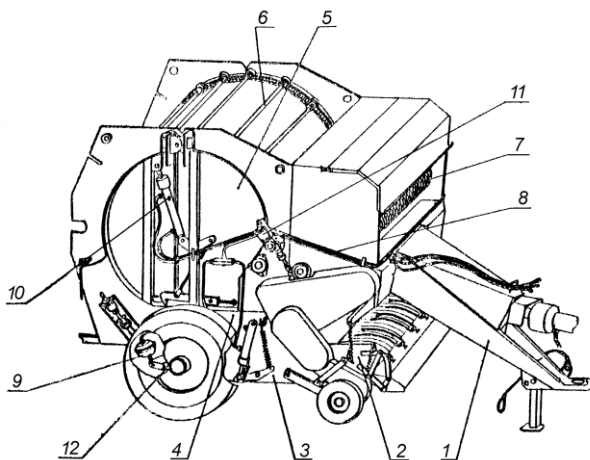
Общий вид пресс-подборщика: 1 – сница; 2 – подборщик; 3 – измельчитель; 4 – основание камеры; 5 – камера прессования; 6 – механизм прессующий; 7 – сетка; 8 – гидропроводы; 9 – привод тормозов пневматический; 10 – гидроцилиндр; 11 – электродвигатель САК; 12 – рычаг стояночного тормоза.
